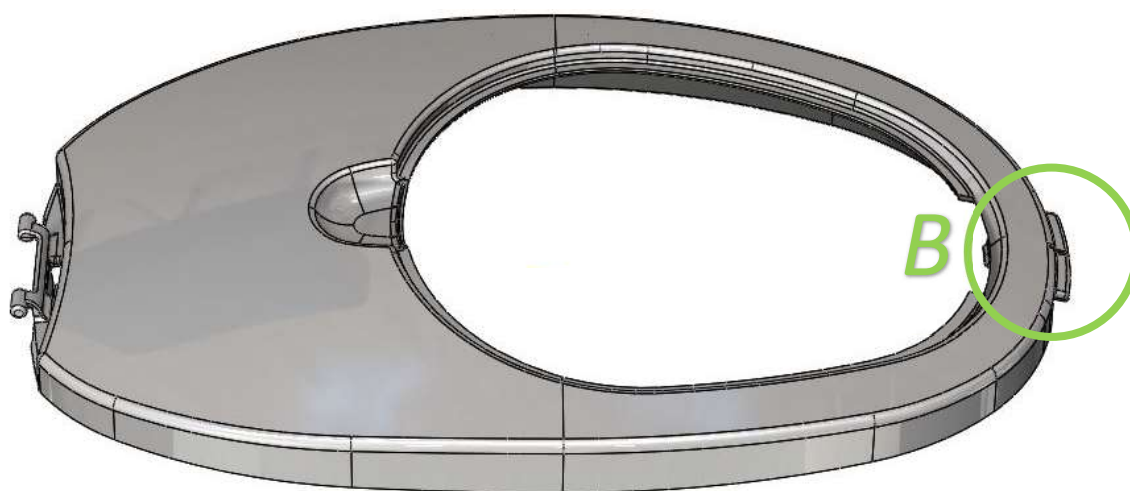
Vista com detalhe do travamento posterior. Fonte: Acervo do autor
